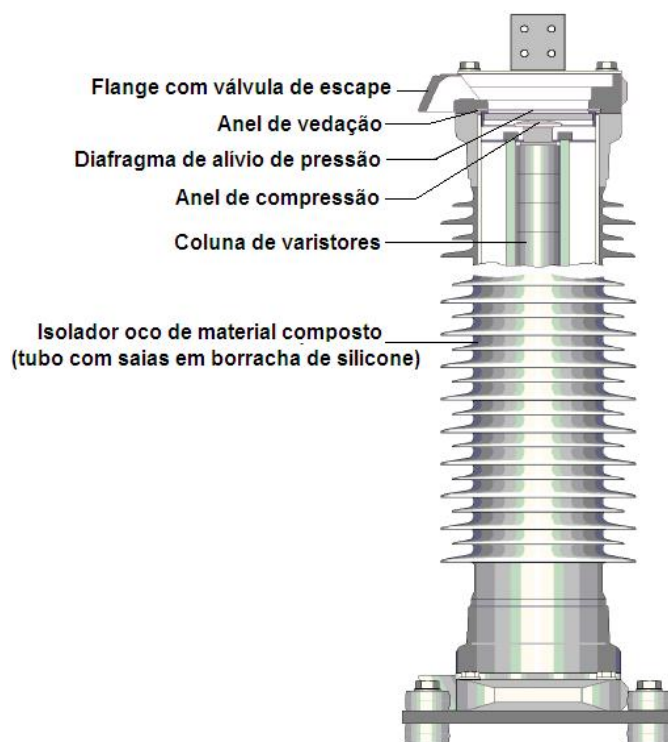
Desenho em corte de um para-raios com invólucro de tubo polimérico
